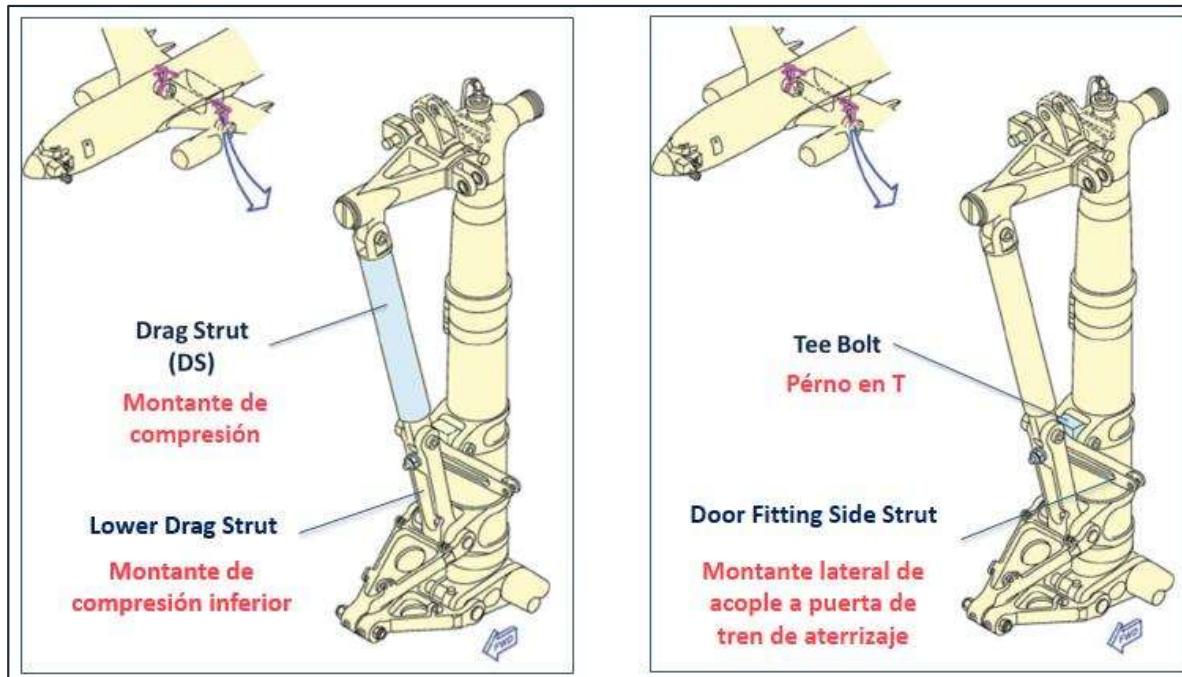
Ubicación del Drag Strut y T Bolt (Esquema Boeing © SB 737-32-1501)
